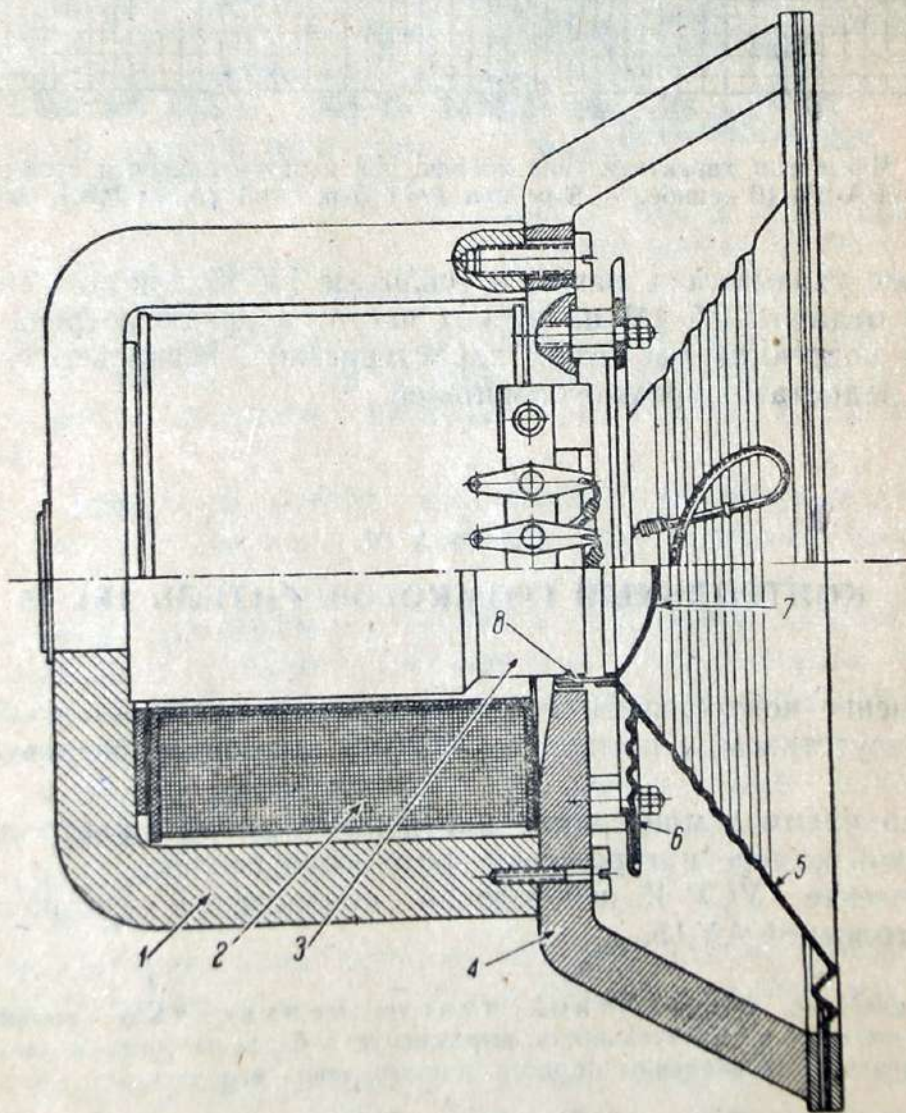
Головка 1А-10 (эскизный чертеж конструкции)
